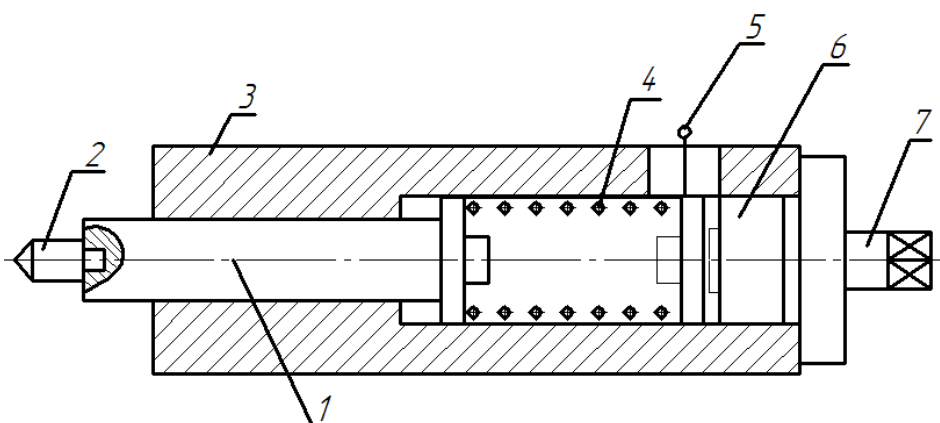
Приспособление для выглаживания рабочих поверхностей вала: 1-шток; 2-выглаживатель; 3- корпус; 4- силовая пружина; 5- индикатор силы выглаживателя; 6 –плунжер; 7 – винт регулировочный.
